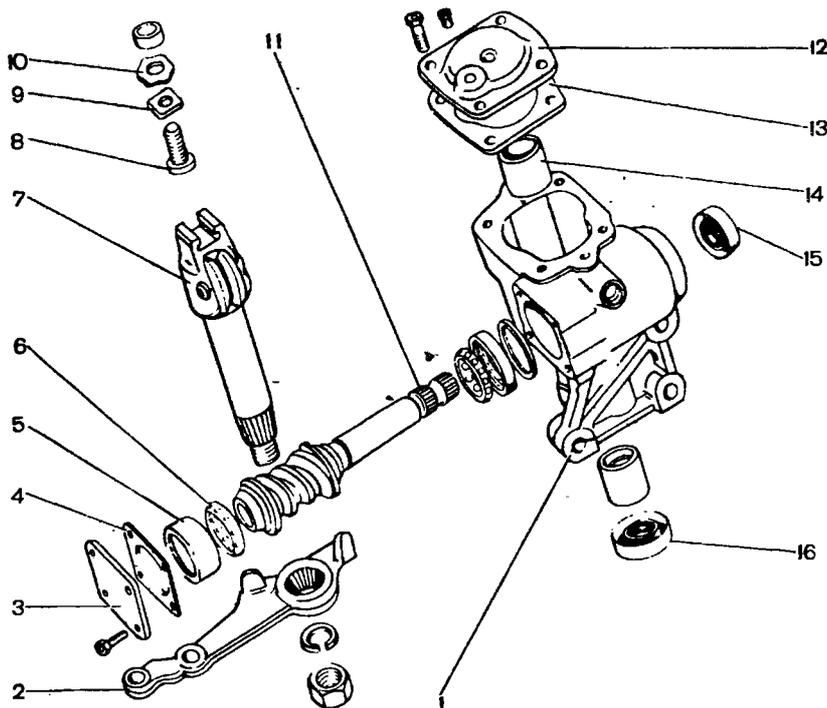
Детали картера рулевого механизма: 1 - картер; 2 - сошка; 3 - нижняя крышка картера; 4 - регулировочные прокладки; 5 - наружное кольцо подшипника вала червяка; 6 - сепаратор с шариками; 7 - вал сошки; 8 - регулировочный винт; 9 - регулировочная пластина; 10 - стопорная шайба; 11 - вал червяка; 12 - верхняя крышка картера; 13 - уплотнительная прокладка; 14 - втулка вала сошки; 15 - сальник вала червяка; 16 - сальник вала сошки
